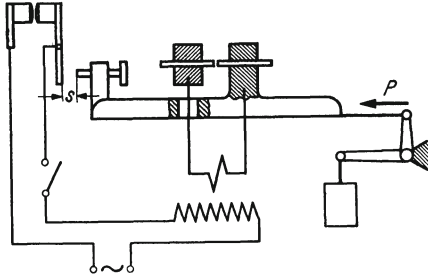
Unterbrechen des Schweißstromes nach einem Stauchweg s bei ruhender Stumpfschweißung.
